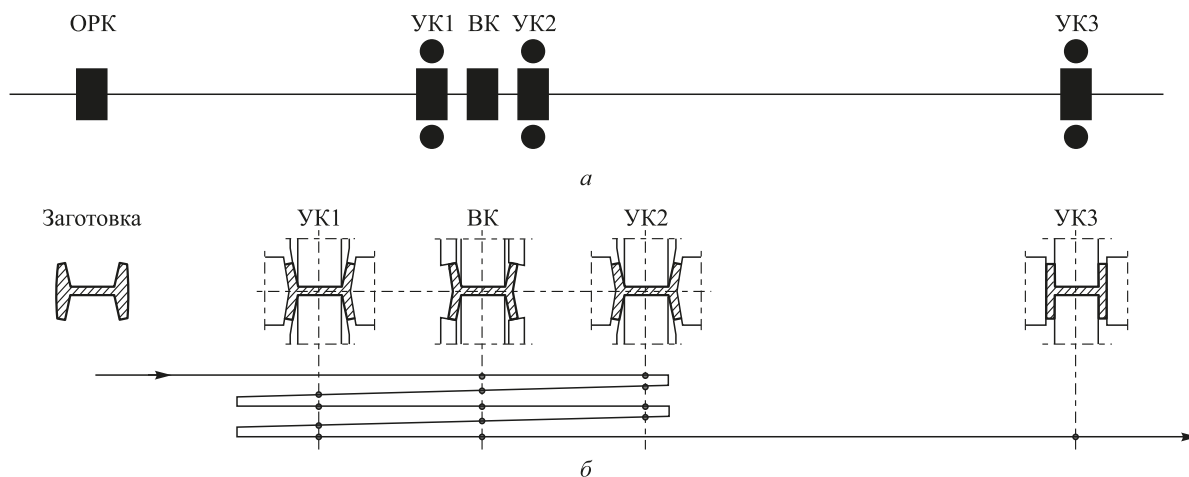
Схемы расположения оборудования (а) и калибровки валков (б) при прокатке двутавровых профилей в чистовой группе клетей универсального рельсобалочного стана:
